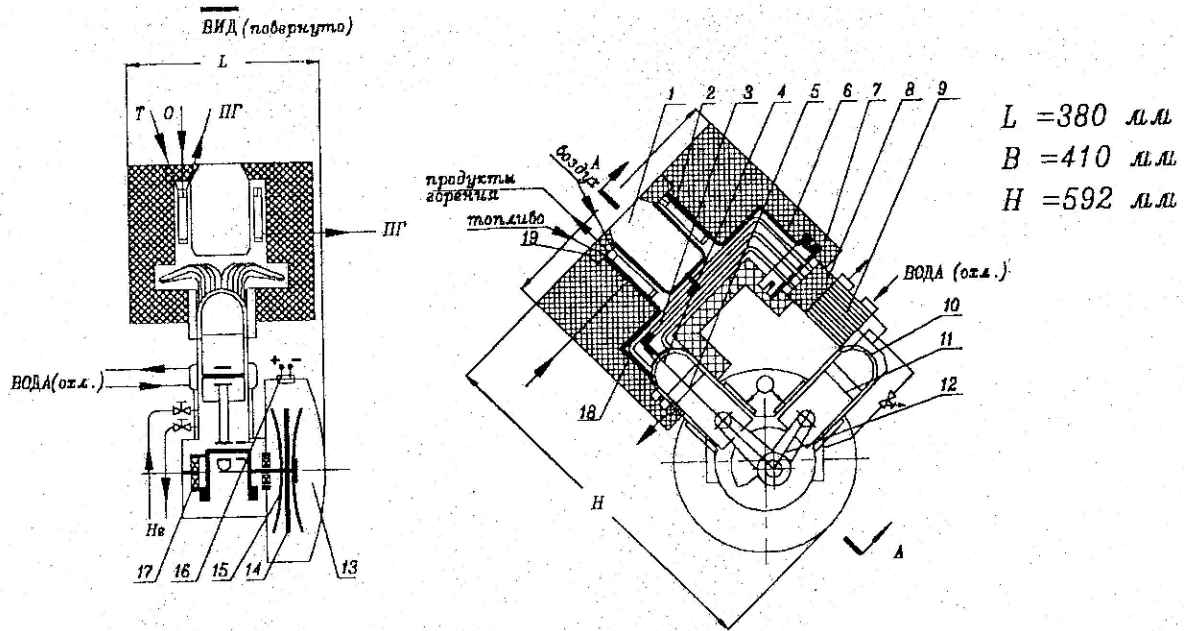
Конструкторская схема Стирлинг генератора для КАЭС: 1 – солнечная ловушка; 2 – корпус камеры горения; 3 – трубка нагревателя; 4 – полость расширения; 5 – поршень вытеснителя; 6 – корпус тепловой трубы; 7 – тепловая изоляция; 8 – регенератор; 9 – холодильник; 10 – полость сжатия; 11 – рабочий поршень; 12 – шатун; 13 – буферная полость; 14 – диск-маховик; 15 – электрогенератор; 16 – гермовыводы; 17 – подшипники; 18 – рабочее тело тепловой трубы (Na-K)
